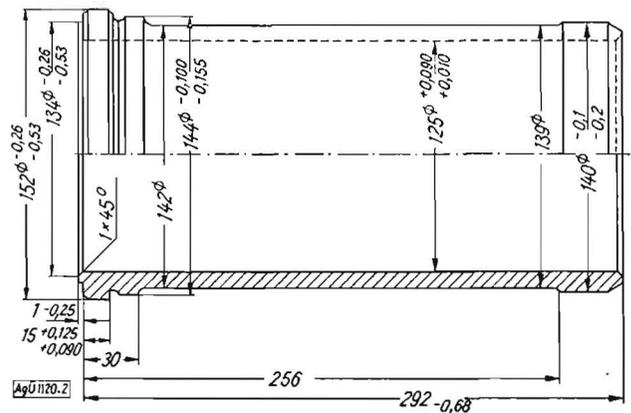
Buchse des Zylinderblocks vom Motor des Traktors DT-54
